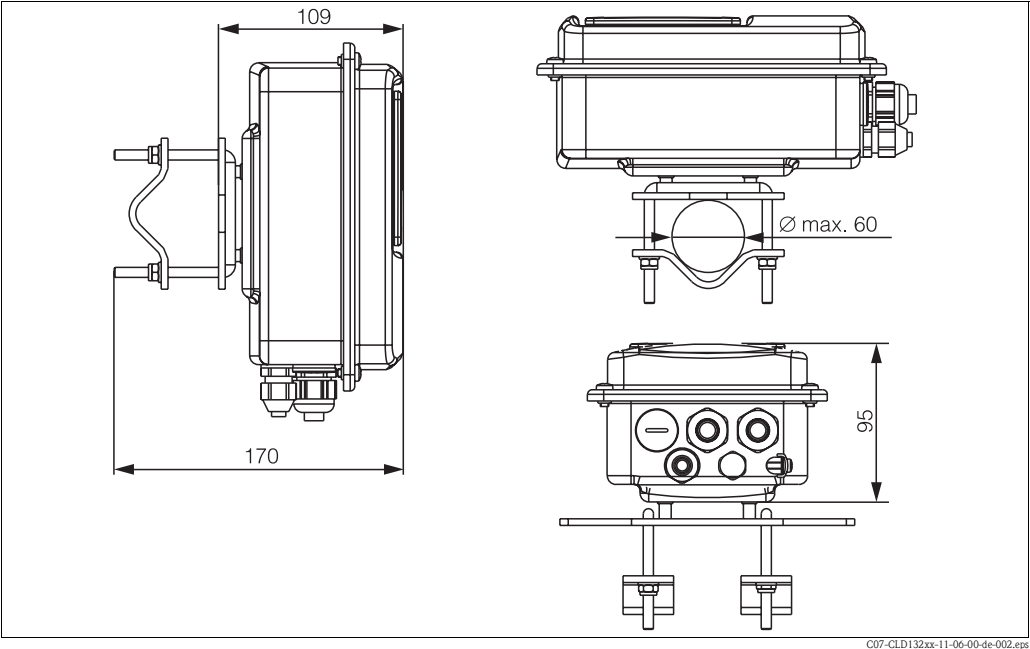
CLD132 pour montage sur tube  $\varnothing 60 \text{ mm}$
